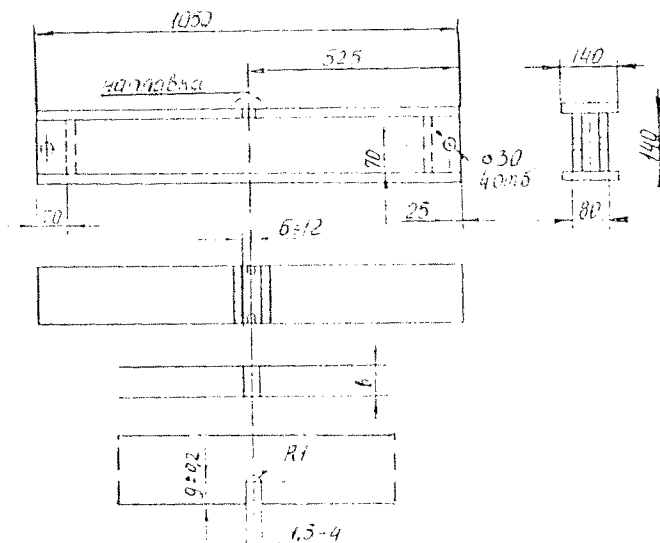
Балочный образец с наплавкой сварочных швов
